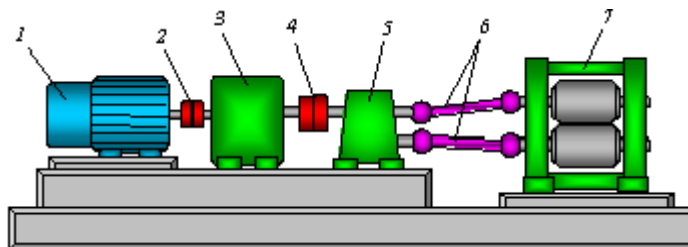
Одноклетьевого прокатный стан: 1 — электродвигатель; 2 — муфта моторная; 3 — редуктор; 4 — муфта коренная; 5 — шестеренная клетка; 6 — шпиндель; 7 — рабочая клетка
